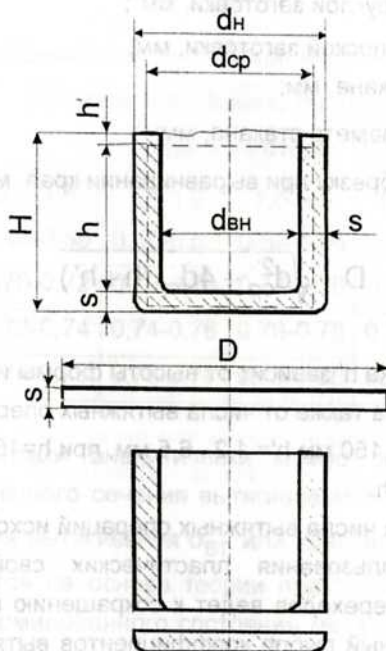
Схема разбивки цилиндрического изделия на элементы при расчете размеров заготовки
